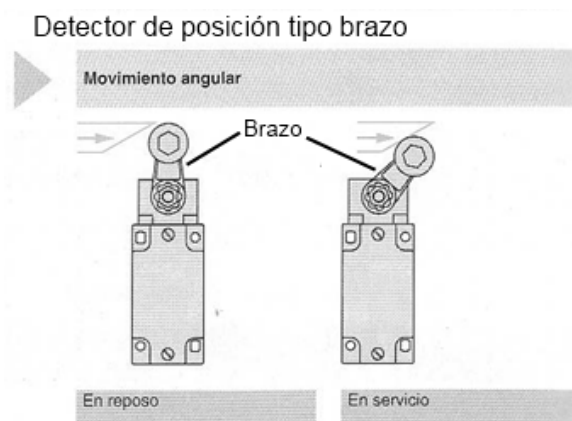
Interruptor de posición que se instalará en el molde, la prensa y en la mesa o banda de bloques terminados de la máquina.
